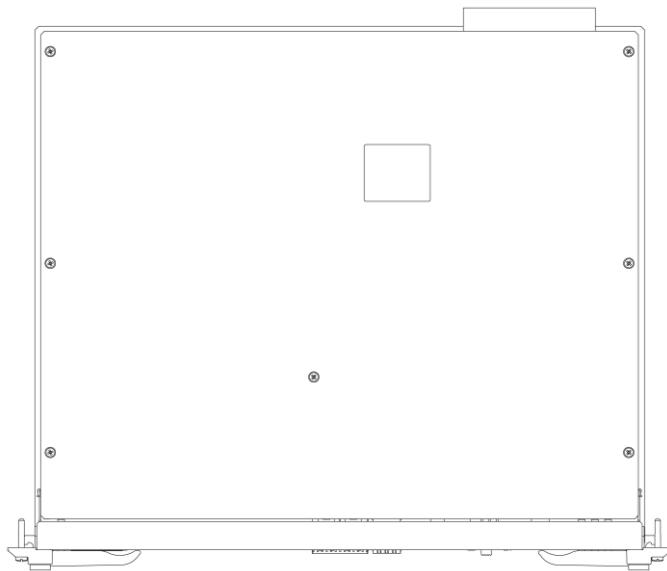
Наклейка закрывающая винт крепления верхней крышки изделия
